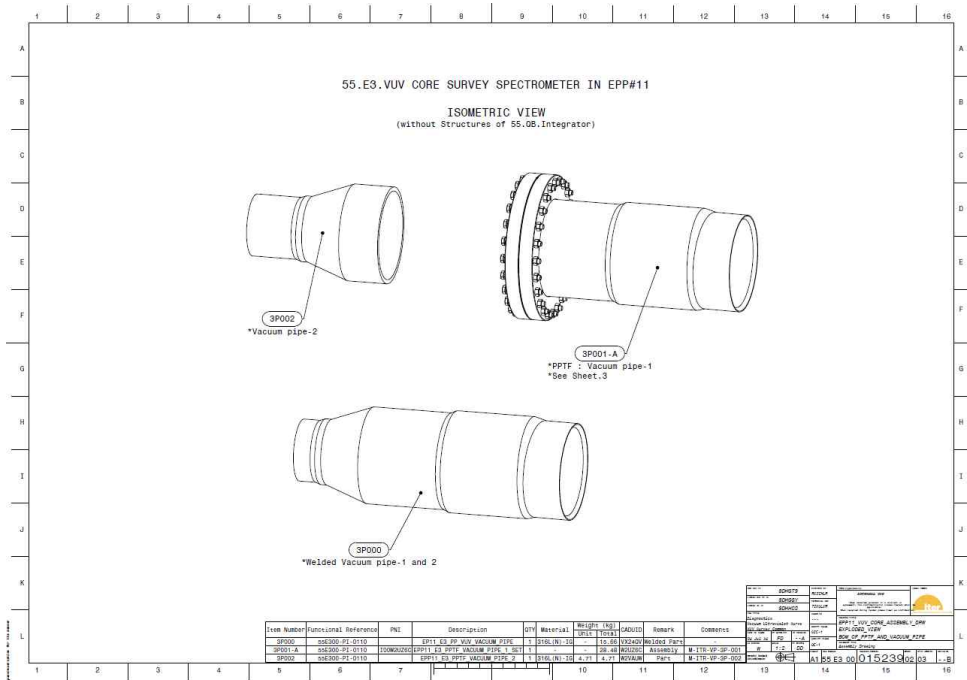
VUV-Core 분광기 Port Plug 내부품 설계 현황, 제작 설계가 마무리 단계이며, 2차원 General Assembly Drawing 및 Installation Drawing 이 현재 작성되어 있는 상황으로 필요 시 수정 계획.
